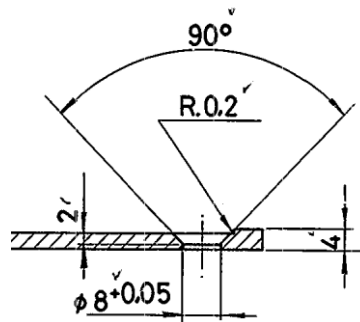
Desenho técnico com diâmetro de 8 mm e tolerância definida pelo cliente.
